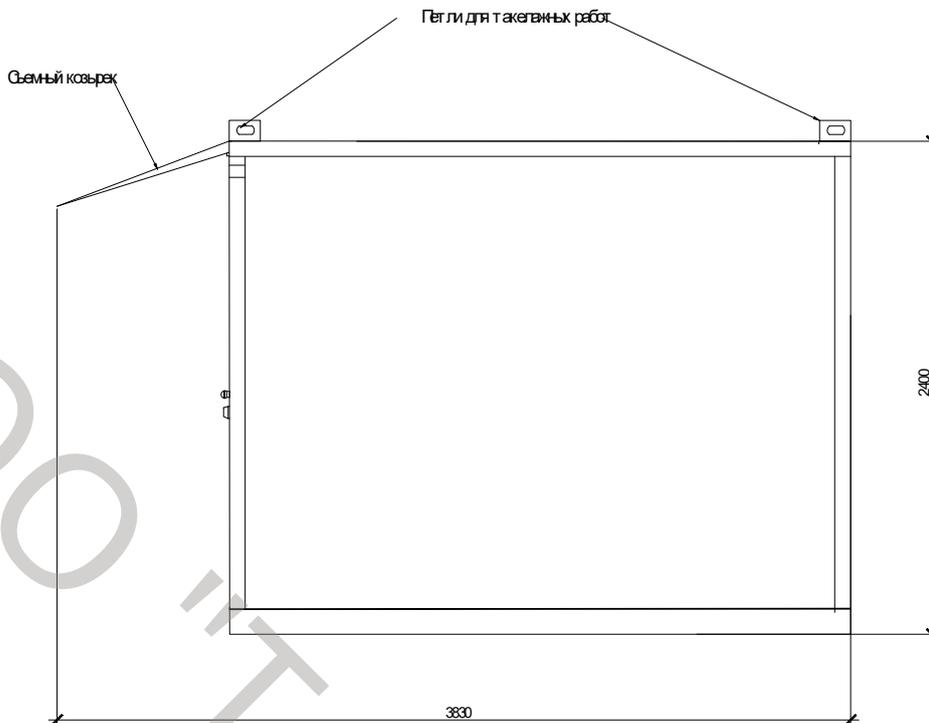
ТШВ-242430БК . Габаритный чертеж. Вид справа.
